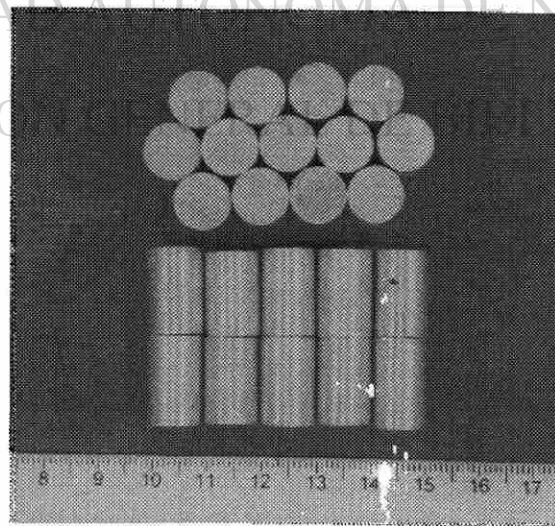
Piezas maquinadas en forma cilíndrica.
